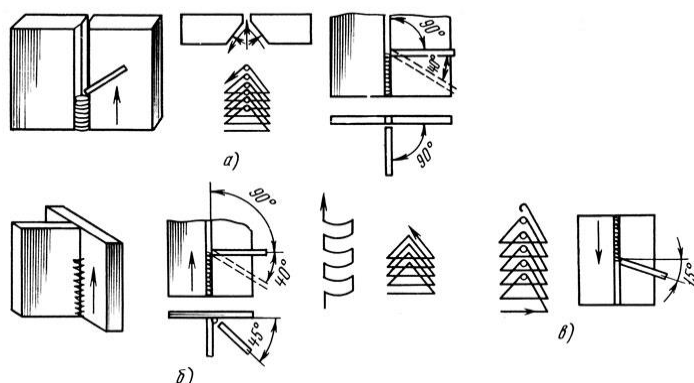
Положение и движения электрода при сварке в вертикальном положении:
